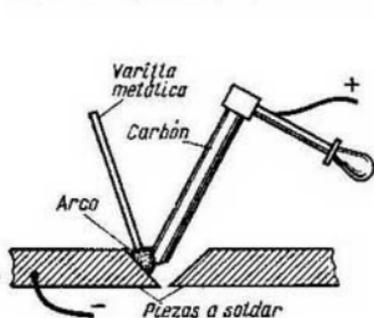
Soldadura eléctrica según el método de Bernardos (con electrodo de carbón)
